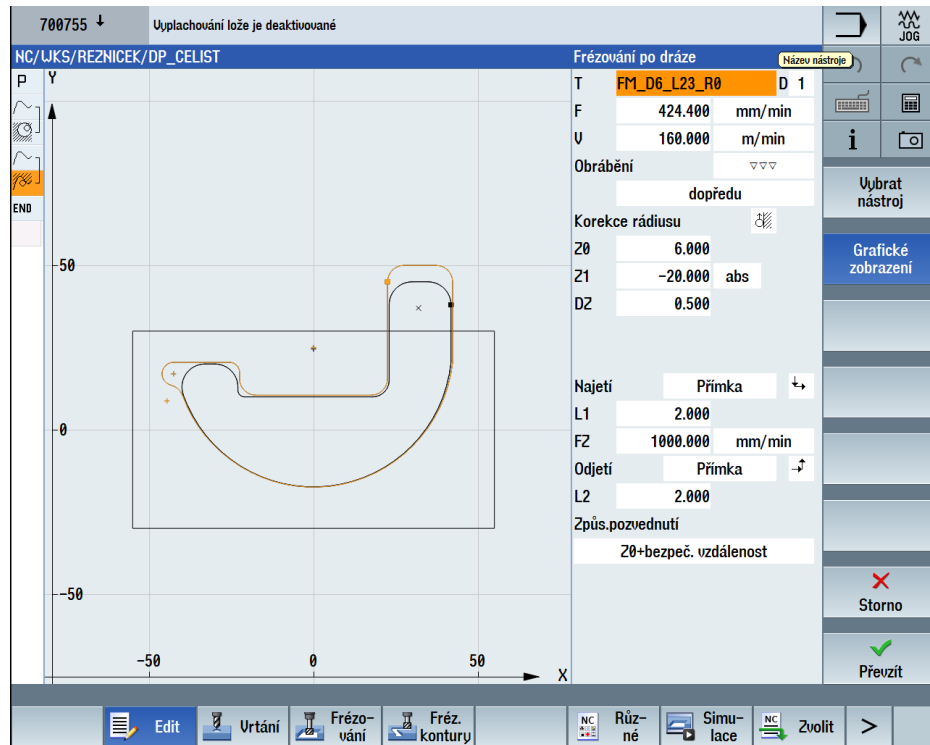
Dráha pro frézování na čisto testovacího přípravku
